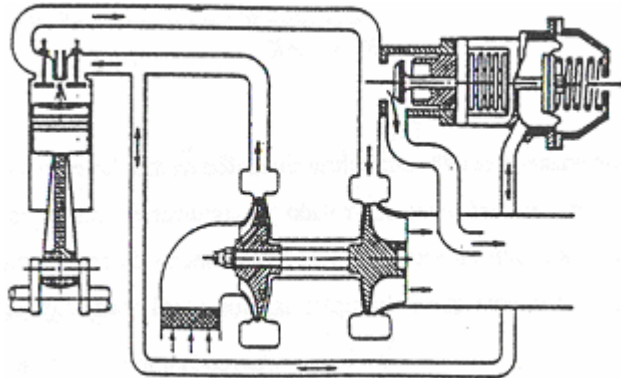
1 – Conjunto wastegate-turbocompressor-motor.
